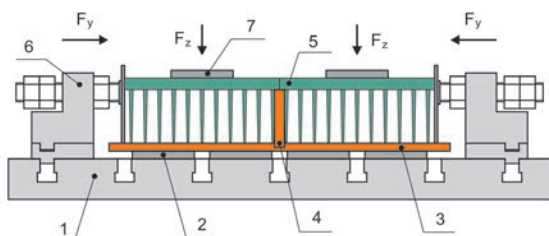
Схема монтажа исходных заготовок охладителя при выполнении сварки
